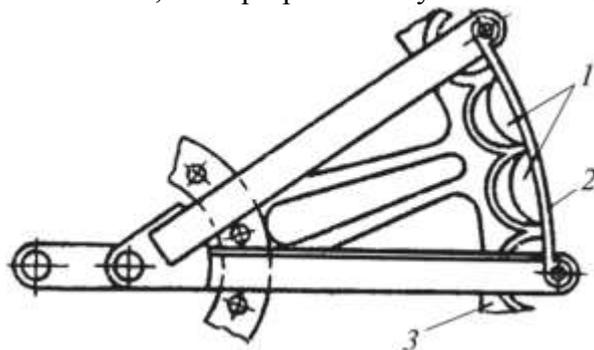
Приспособление для наплавки зубьев звездочки:
